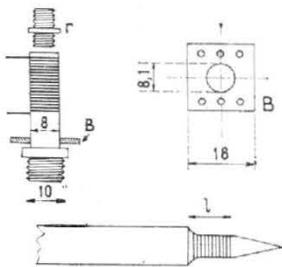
Mandrin Lipa 7MB75 avec la vis de recordement destinée à fixer deux mandrins bout à bout. En B, la pièce de la figure 486
